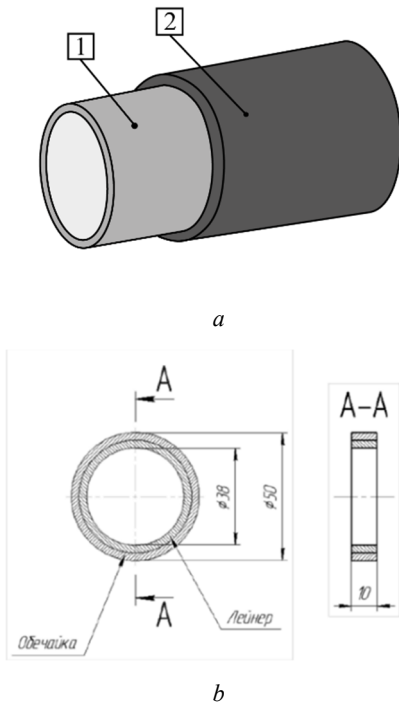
Образец биметаллической НКТ: *a* – внешний вид цилиндра: 1 – лейнер (внутренняя часть); 2 – обечайка (внешняя часть), *b* – эскиз исследуемых образцов
